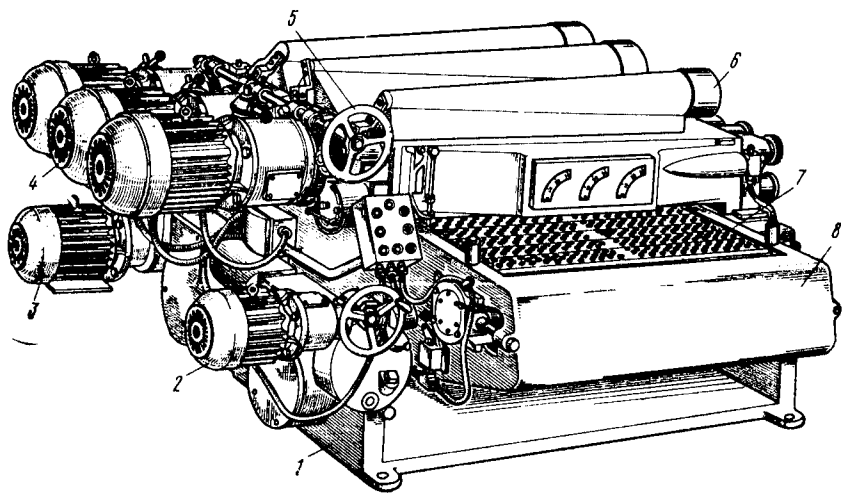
Шлифовальный трехцилиндровый станок ШЛ3Ц12-2
